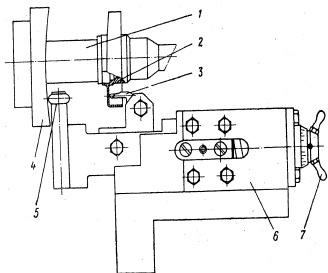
Схема наладки станка для обработки торцов деталей по криволинейному контуру.
